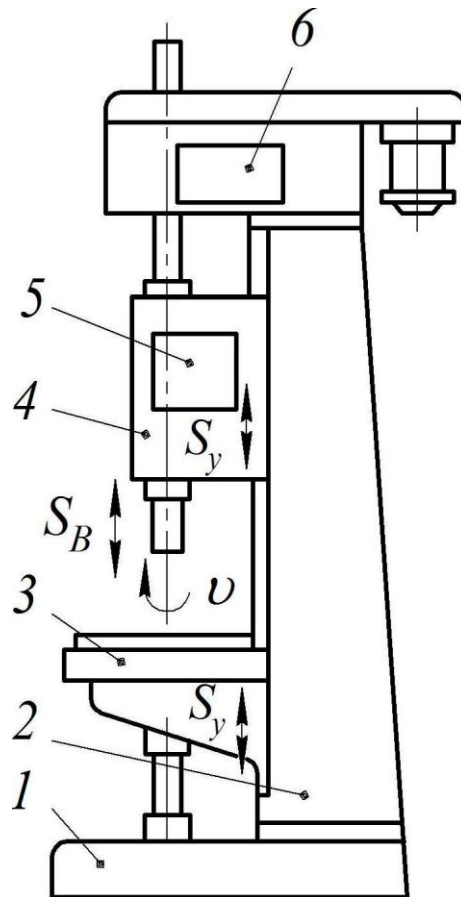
Загальний вигляд вертикально-свердлильного верстата
